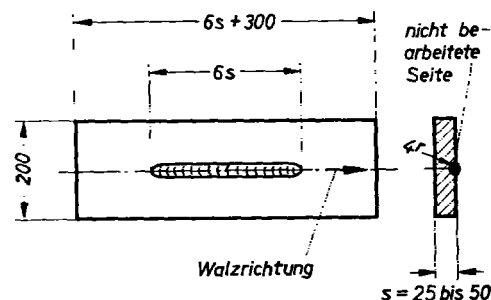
Probe für den Aufschweißbiegeversuch
